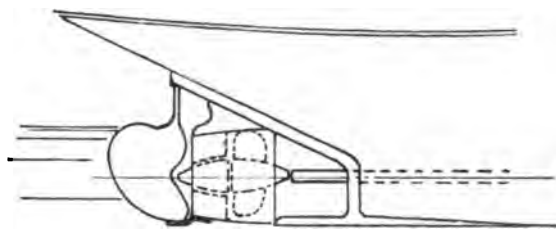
Turbinenschraube von Holtz an einem Einschraubenschiffe.
